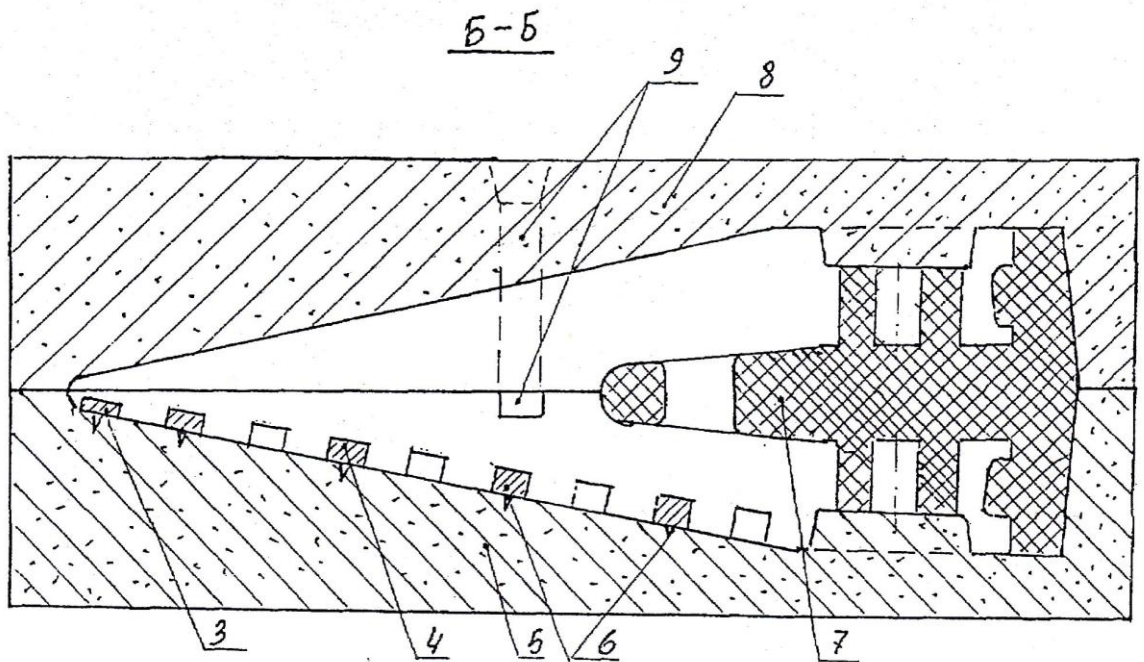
Литейная форма для отливки коронки рыхлителя
